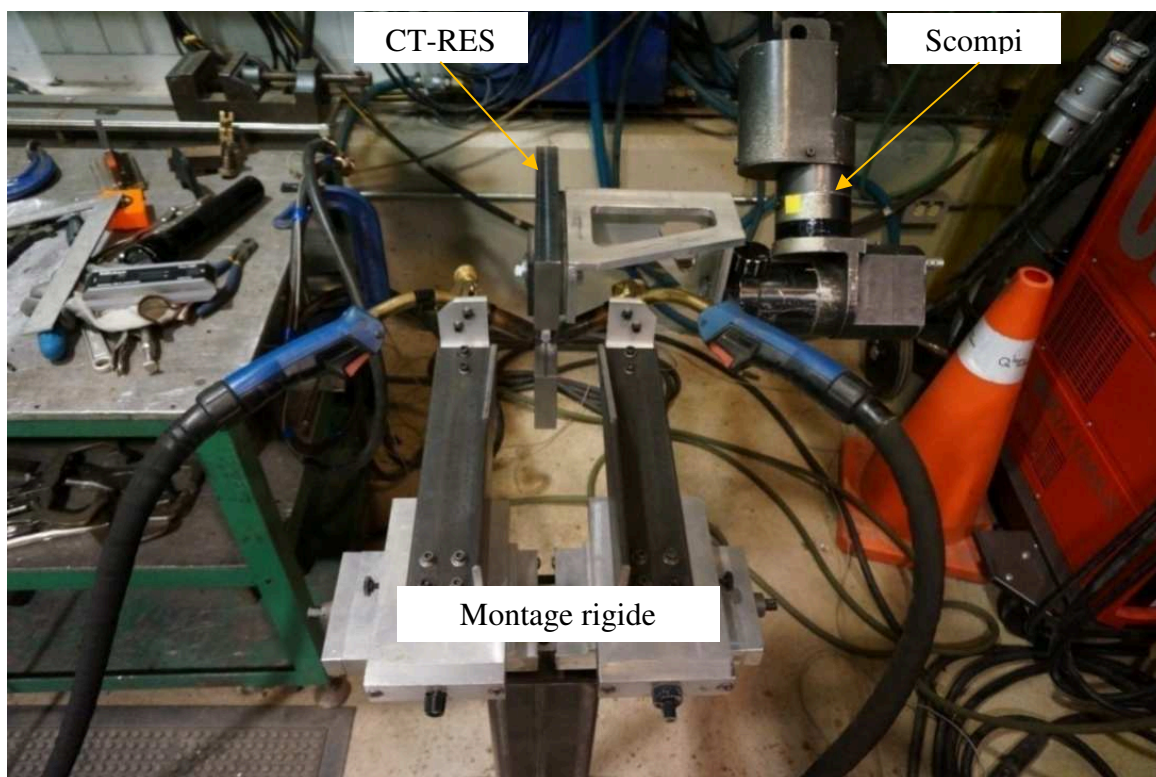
Montage utilisé lors du soudage des éprouvettes CT-RES avec Scompi®
